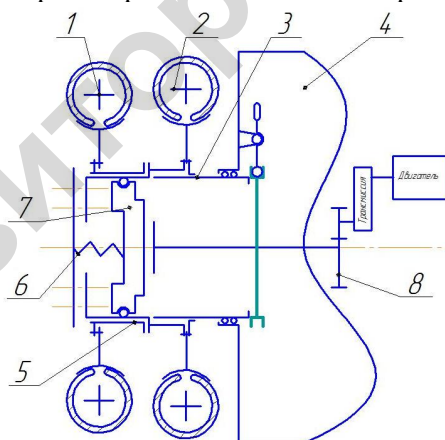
Опорно-сцепного устройства для сдваивания задних колес трактора «БЕЛАРУС»:
